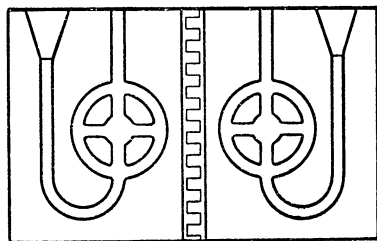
Складной алюминиевый кокиль для отливки колесика.
